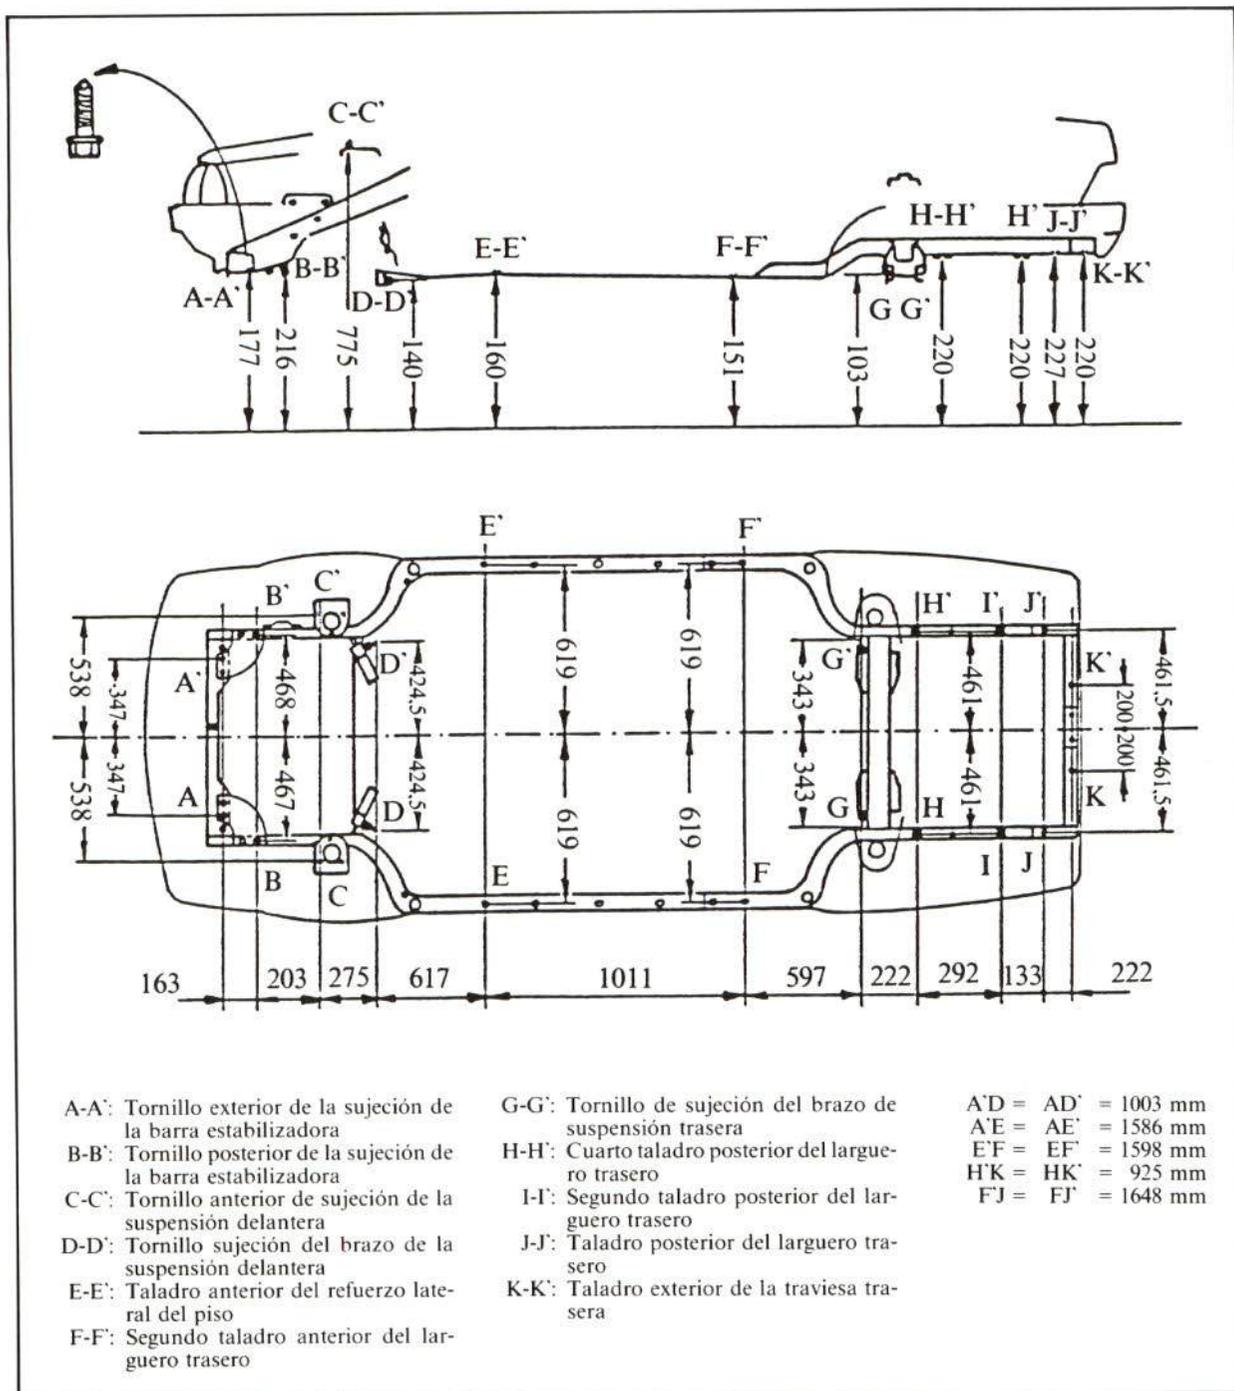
Dimensiones del vehículo en planta y alzado.
